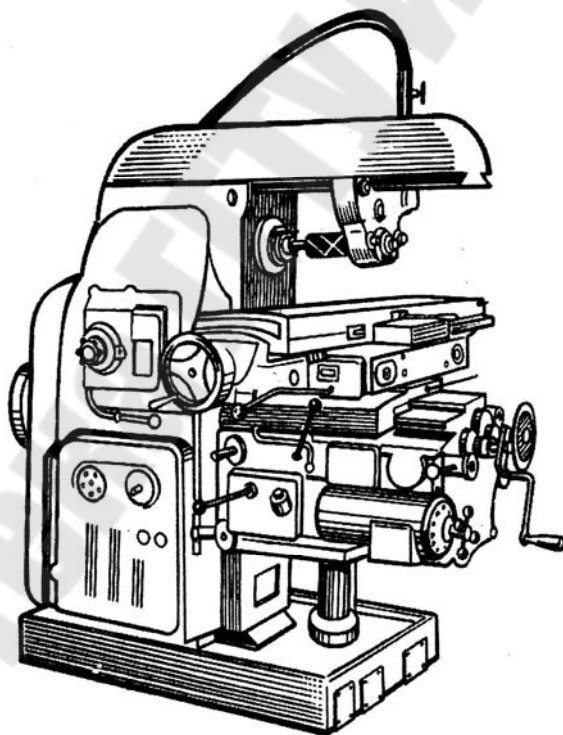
Внешний вид универсального консольно-фрезерного станка модели 6Н82
